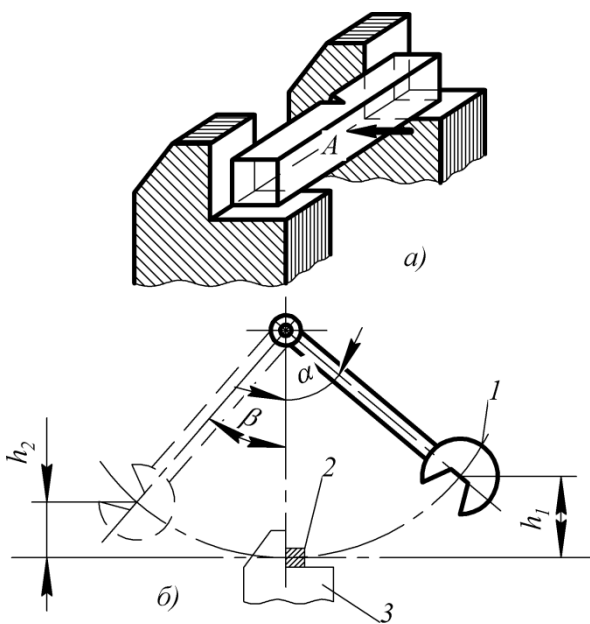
Испытание на ударный изгиб образца с надрезом: а – расположение образца; б – схема нанесения удара; А – направление удара;
